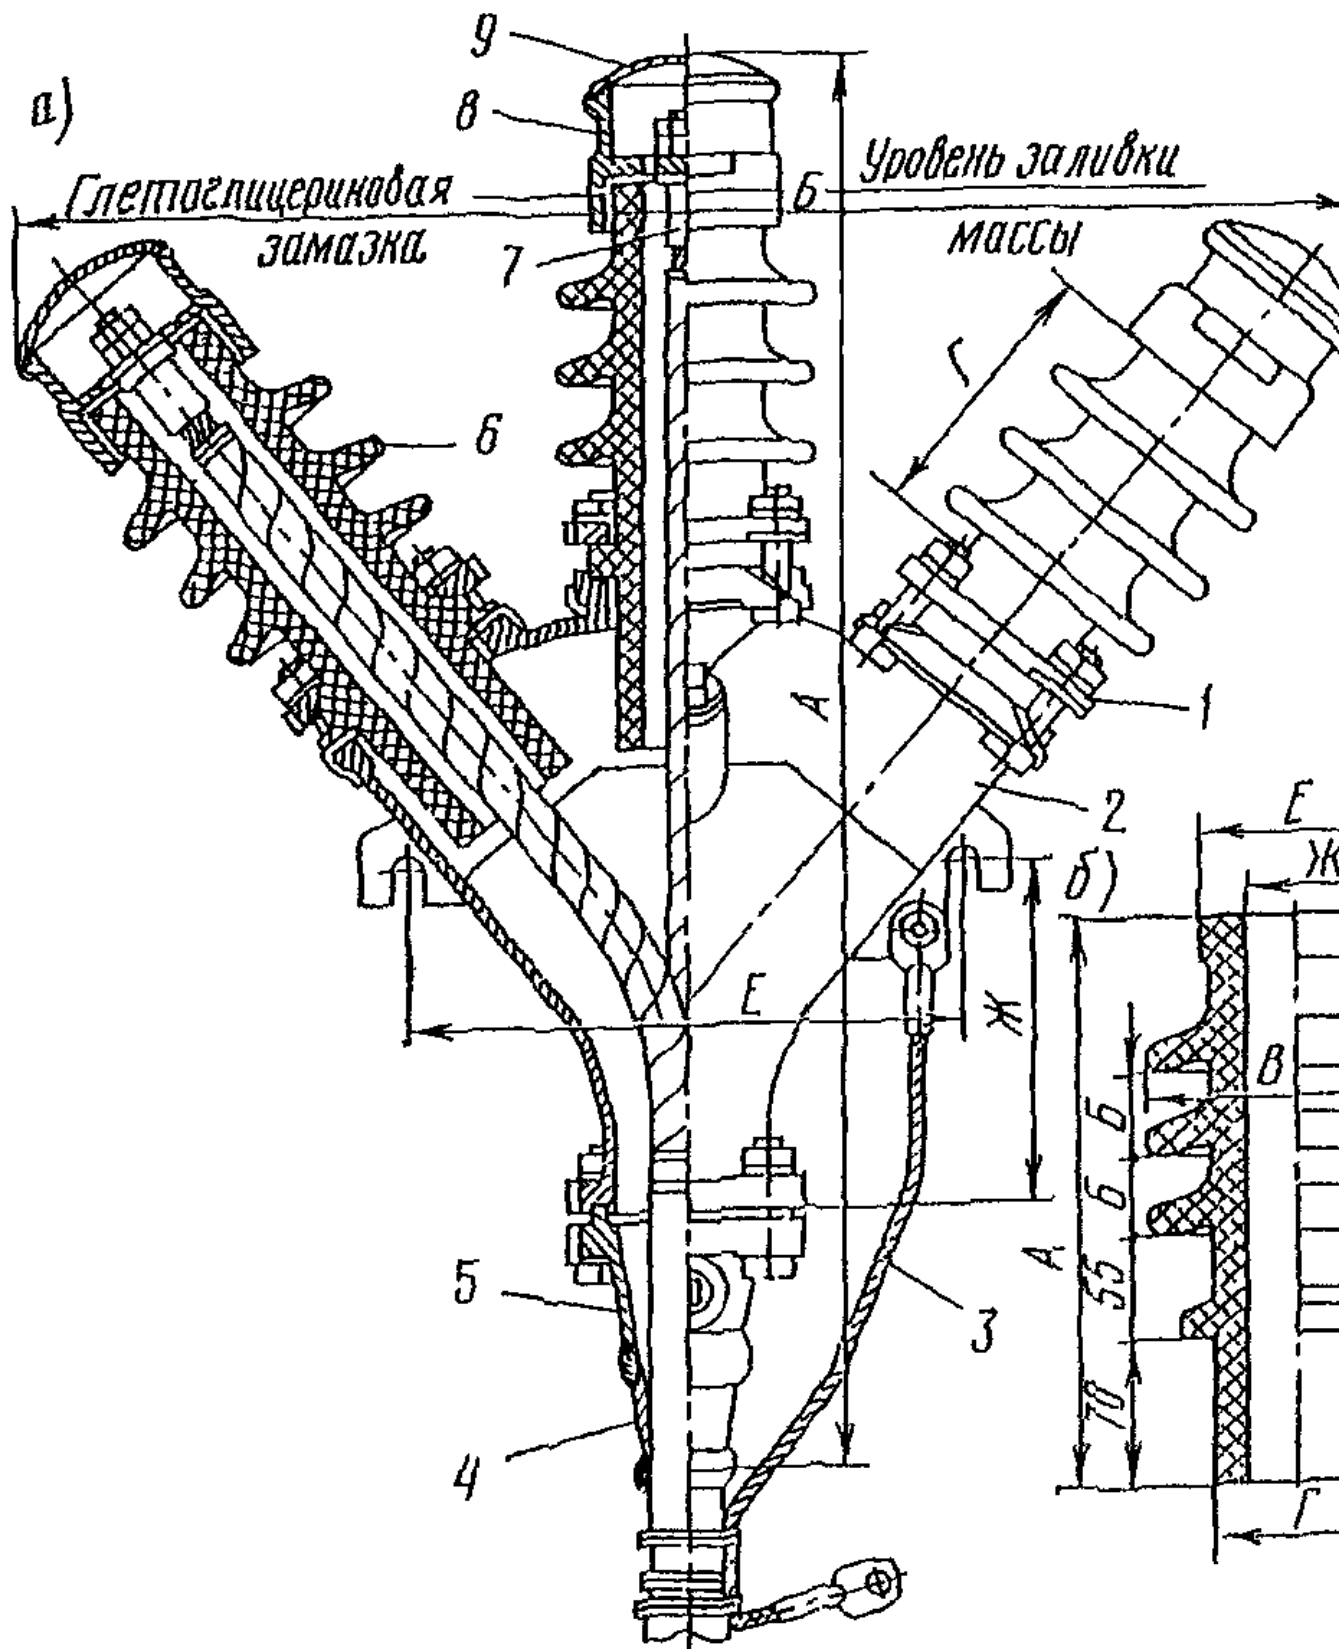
Концевая трехфазная муфта типа КН: а - муфта; б - изолятор фарфоровый; 1 - латунное или алюминиевое полукольцо; 2 - корпус; 3 - провод заземления; 4 - свинцовая манжета; 5 - конус; 6 - изолятор; 7 - наконечник; 8 - контактная головка; 9 - медный колпачок
